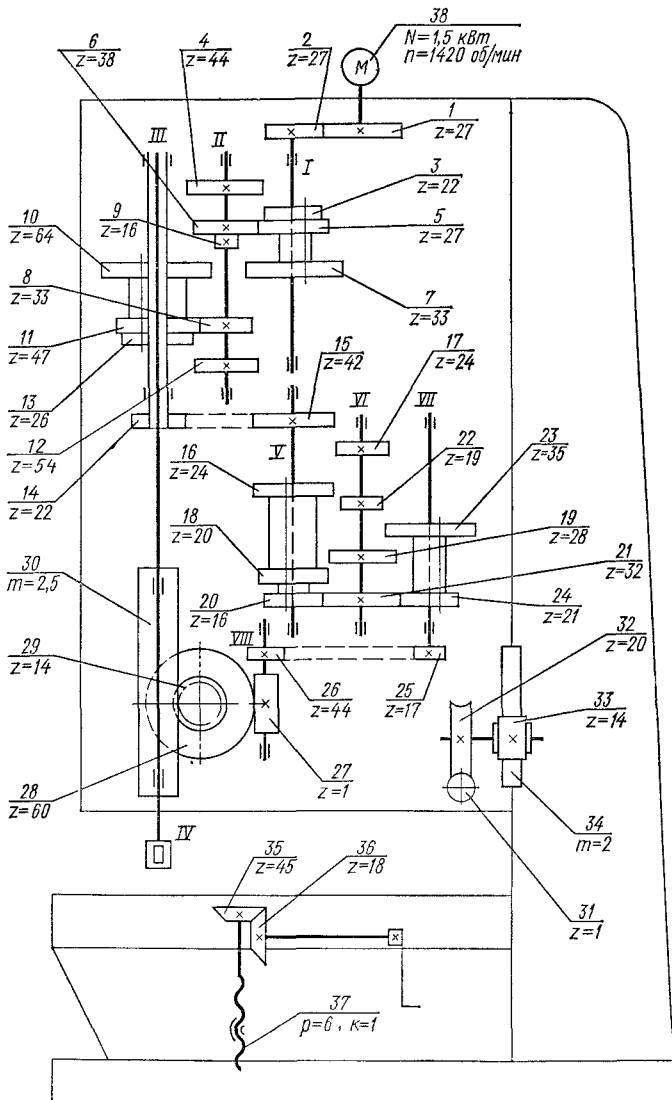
Кинематическая схема вертикально-сверлильного станка мод. 2Н118
